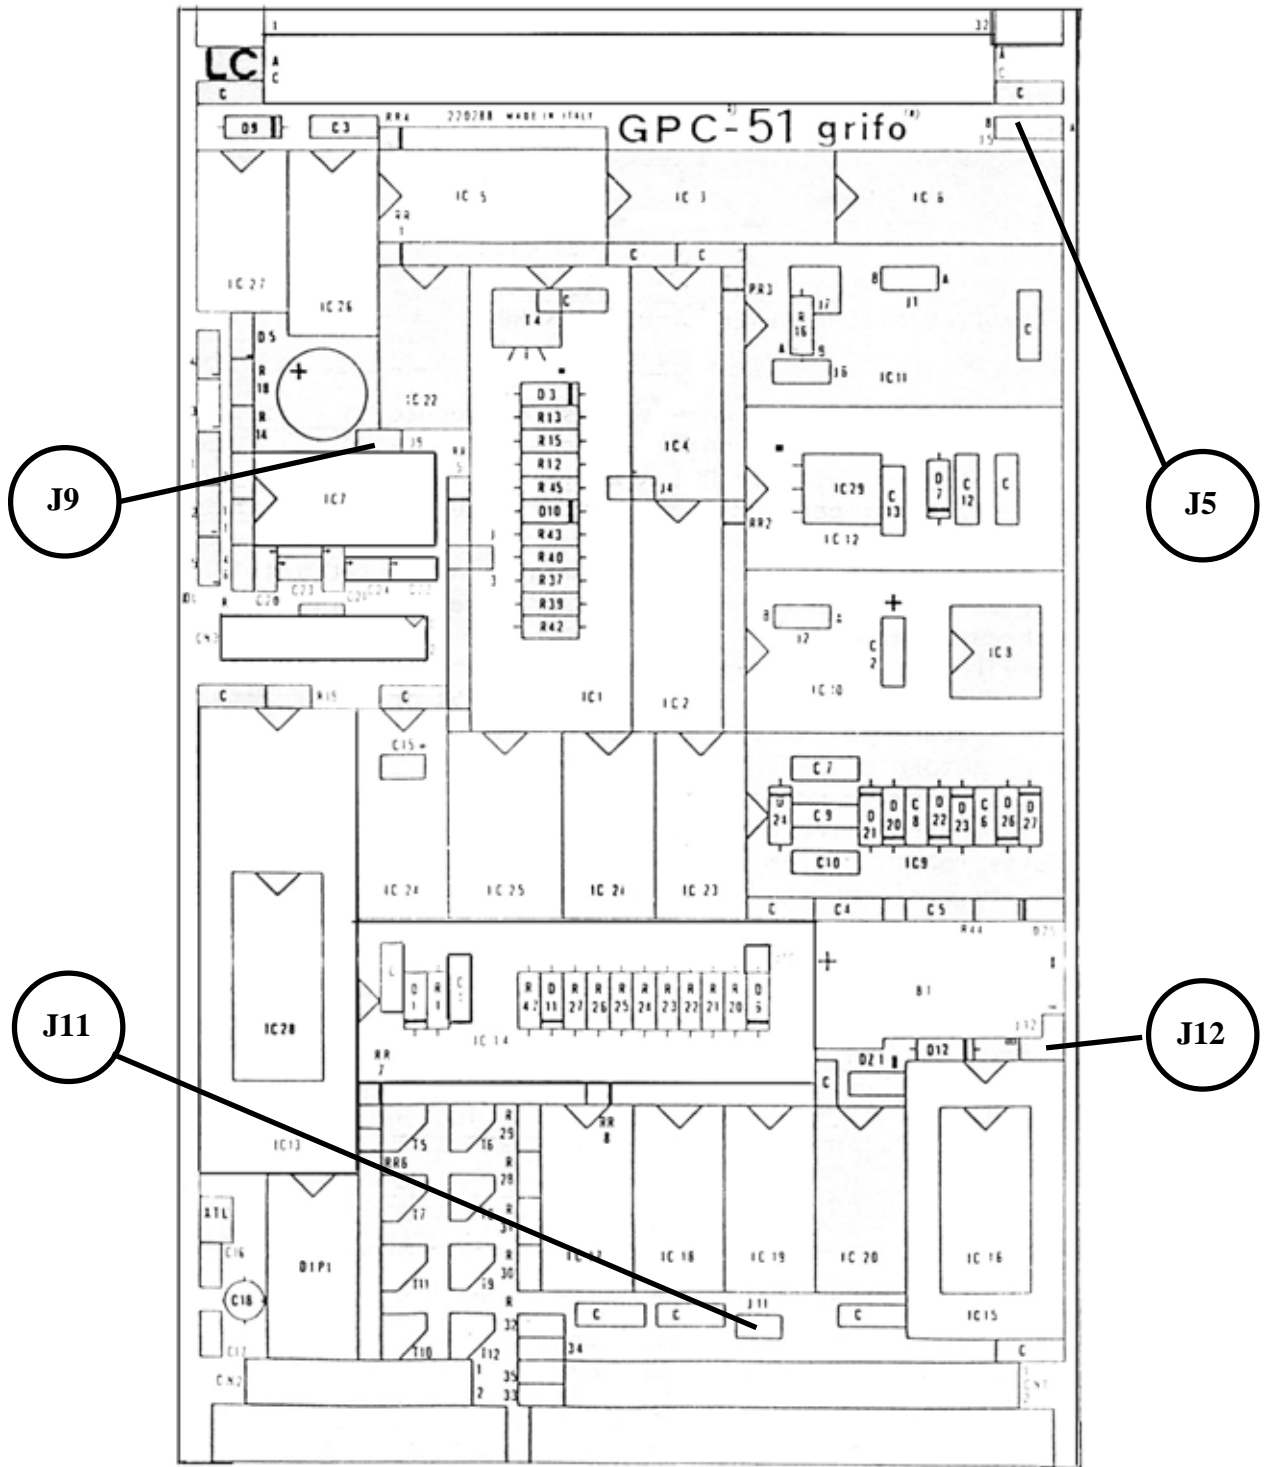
DISPOSIZIONE JUMPERS LATO COMPONENTI
